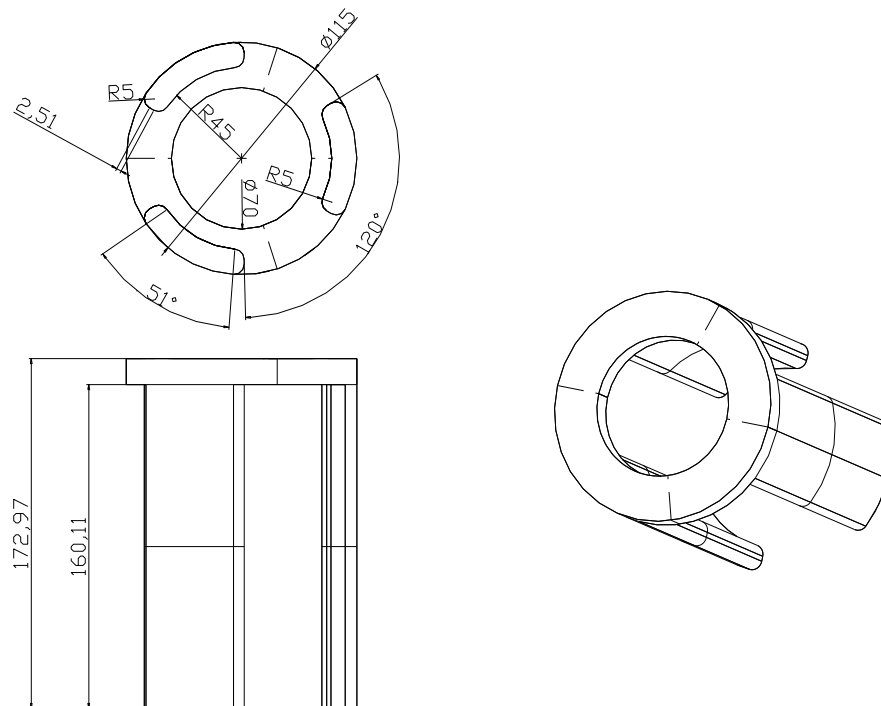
Dimensiones de la pieza que se acopla en el centro de la cadera y que será la fijación del cuerpo superior del robot a la cadera. (Unidades en mm)
